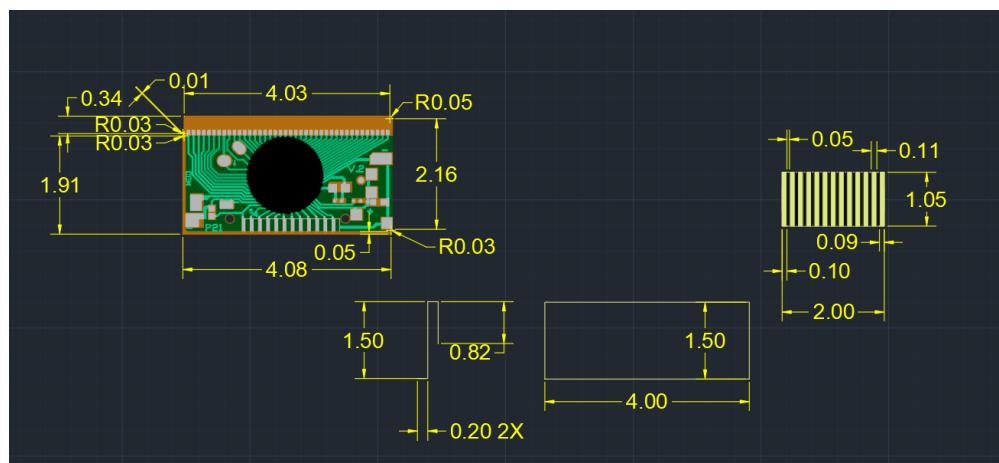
PCB-ul și cele două benzi cu care este prins de ecran cu cotare
